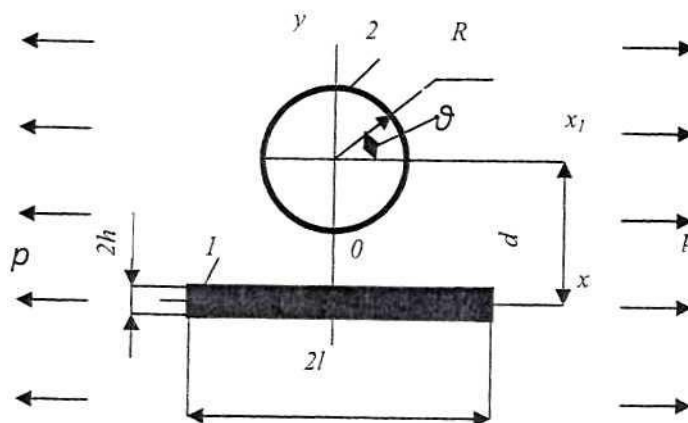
Схема взаимодействия сварного шва и концентратора напряжений в пластине
